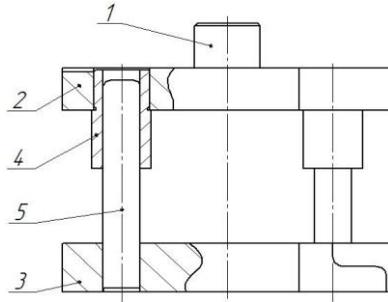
Элементы блока штампа с направляющими колонками:
